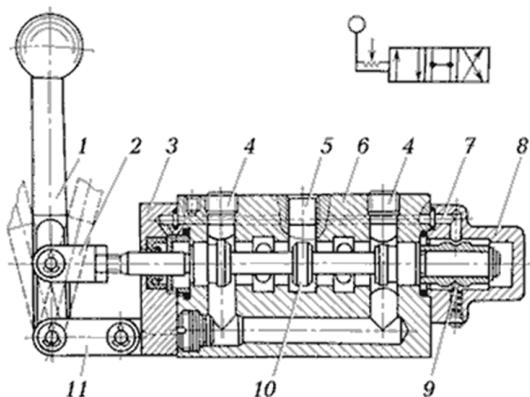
Схема и устройство ручного гидрораспределителя
